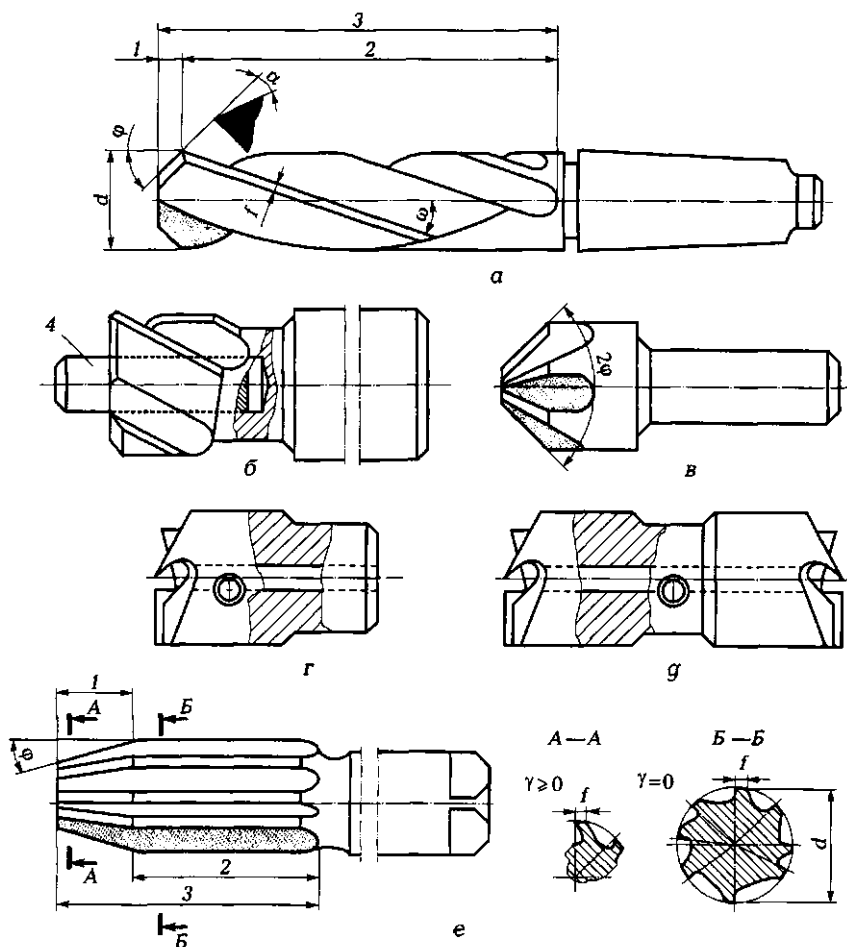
Зенкеры, цековки, зенковки и развертки:
